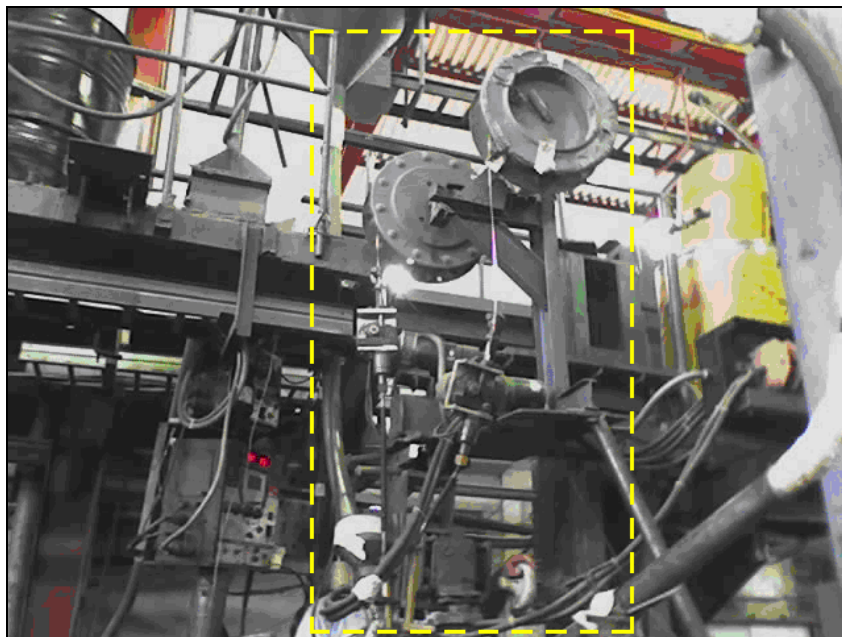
Se muestra los excesos de componentes que integran la base de cabezal de soldadura actual. El cuadro enmarcado de amarillo señala la base del cabezal de soldadura actual
